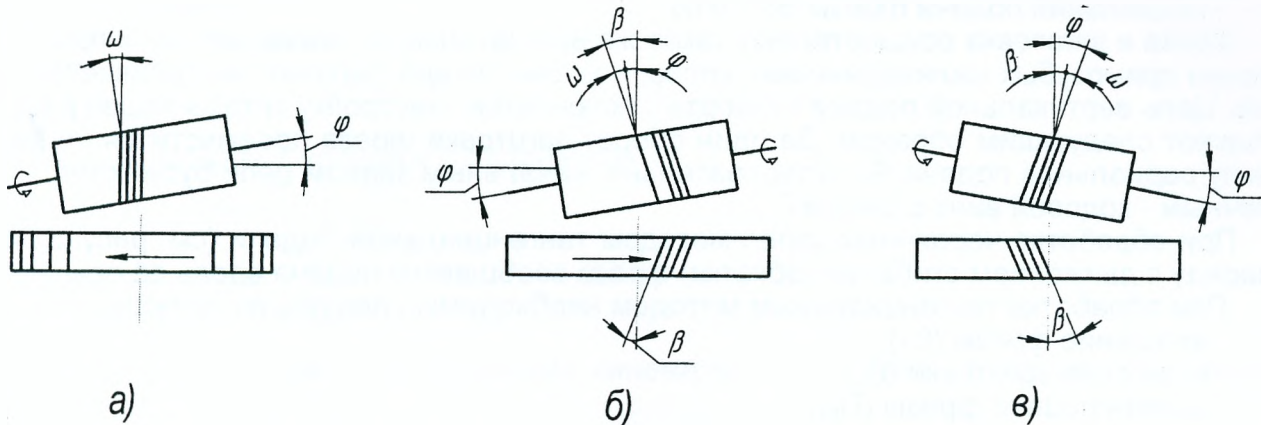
Схема наладки на зубофрезерование зубчатых колес:
